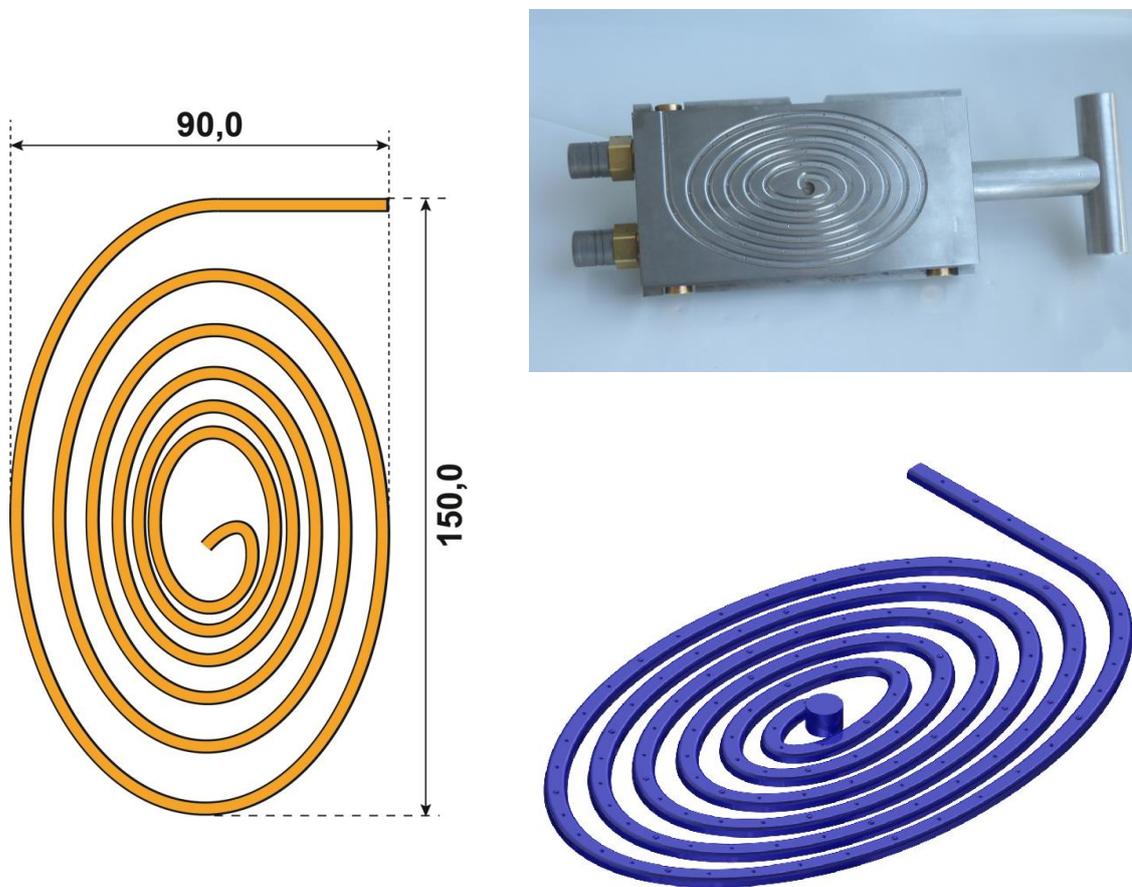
Probengeometrie, Werkzeugkassette und Bauteil der „Fließspirale“
